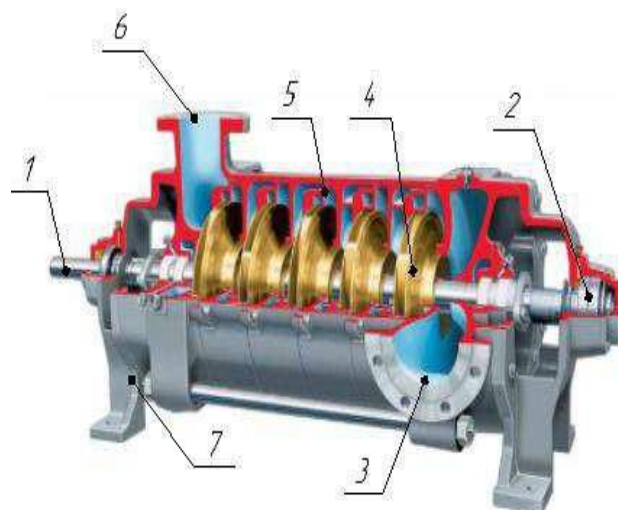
Центробежный компрессор: 1 – вал; 2 – подшипники;
